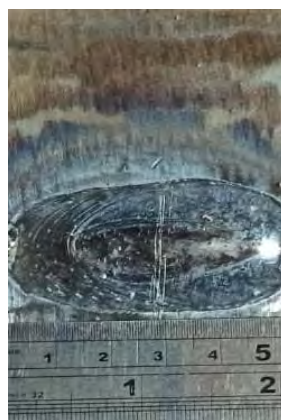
Aspecto exterior del cordón de soldadura - Prueba 2
